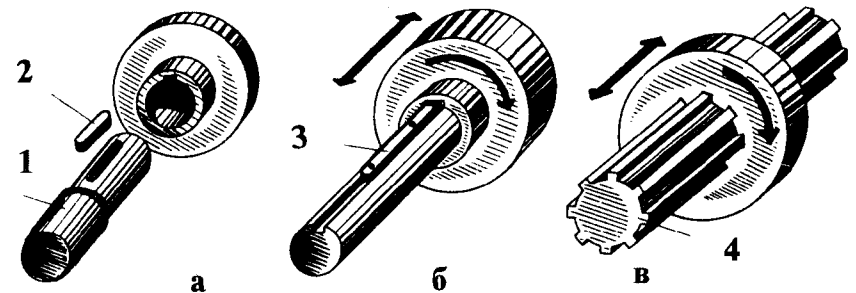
Соединение колеса с валом: а — шпоночное неподвижное; б — шпоночное, скользящее, с поступательным движением вдоль оси; в — шлицевое, скользящее, с поступательным движением вдоль оси: 1 — вал, 2 — шпонка, 3 — скользящая шпонка, 4 — шлицевый вал
